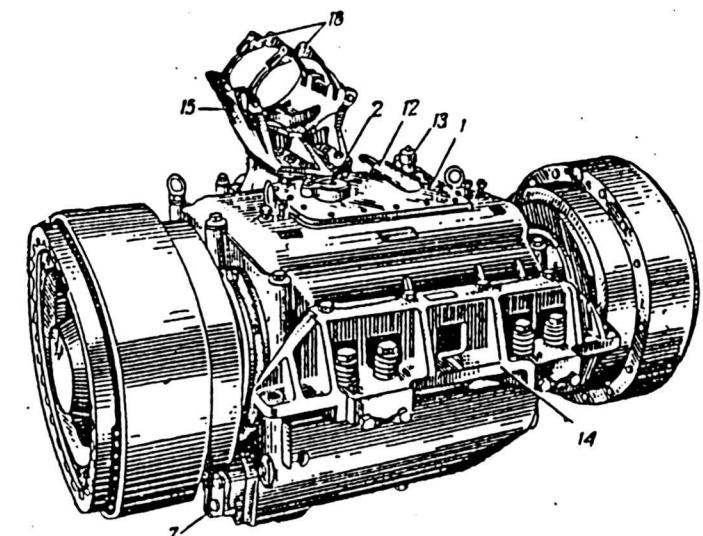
Коробка передач с механизмами поворота (общий вид сзади):
